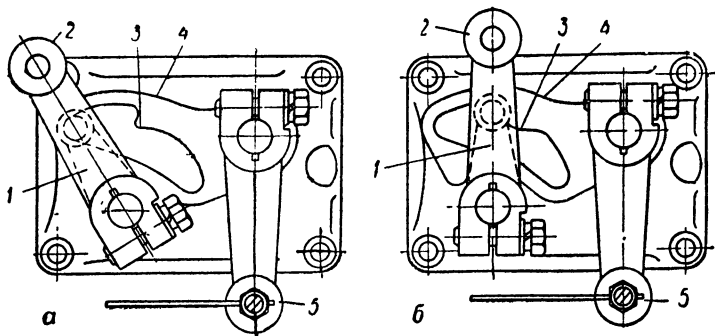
Схема положения рычагов управления подачей топлива: а — наибольшая подача топлива; б — холостой ход; 1 — рычаг, ограничивающий подачу топлива; 2 — рычаг управления подачей топлива; 3 — прорезь; 4 — ограничительный сектор; 5 — рычаг остановки двигателя
